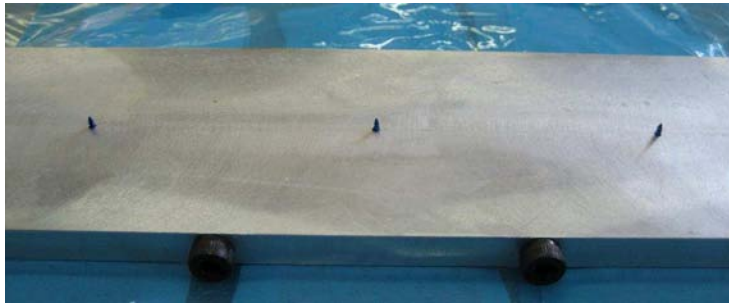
Outil métallique pour assurer la perpendicularité des vis
